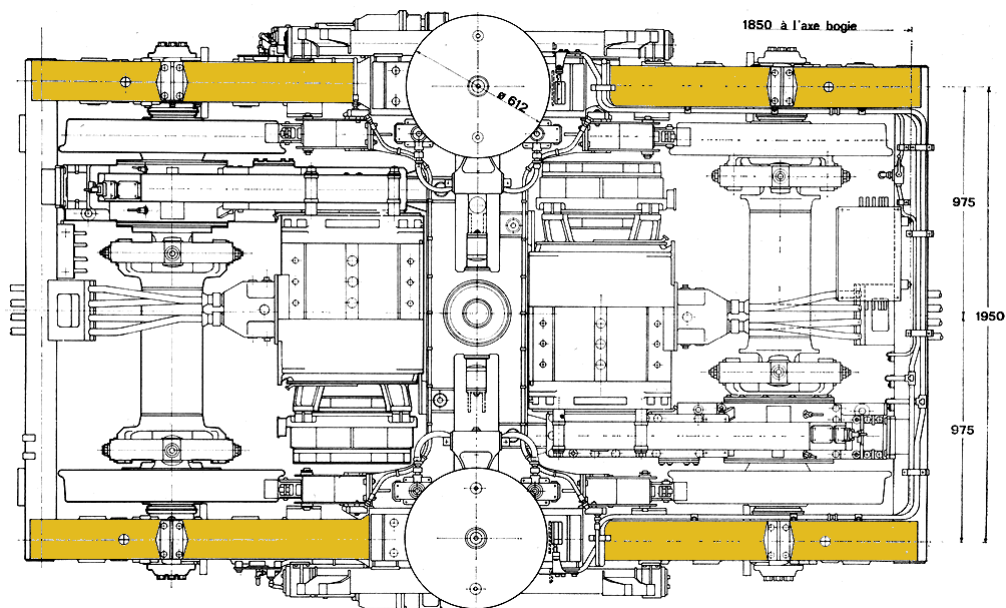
vue de dessus du dessin d'ensemble d'un bogie de TGV
